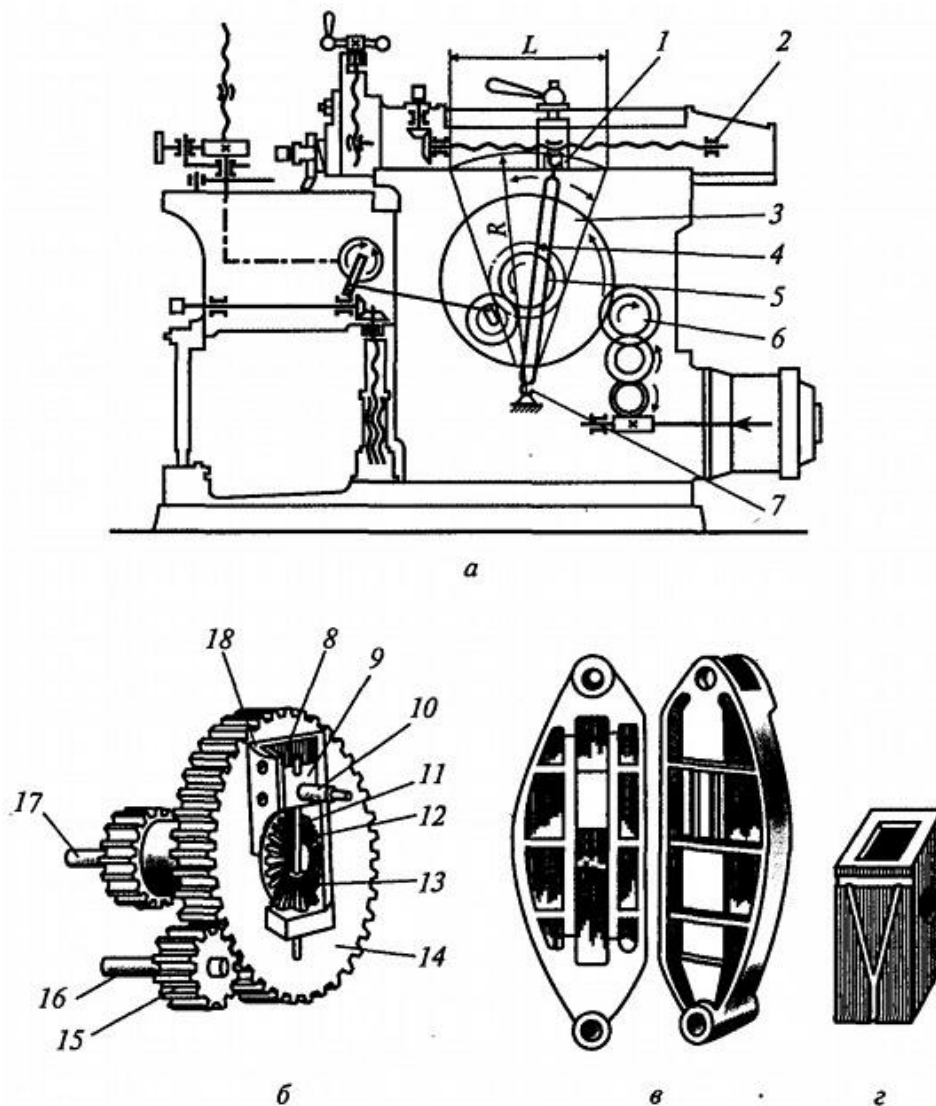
Схемы кулисного механизма (а), механизма регулирования и установки кулисного камня (б) и общий вид кулисы (в) и кулисного камня (г): 1 и 7 — серьги; 2 — ползун; 3 и 14 — зубчатые колеса; 4 — кулисный камень; 5 — кулиса; 6 и 15 — шестерни; 8 — клин; 9 — ползунок; 10 — ось; 11 — винт; 12 и 13 — конические зубчатые пары; 16 и 17 — валы; 18 — направляющее устройство
